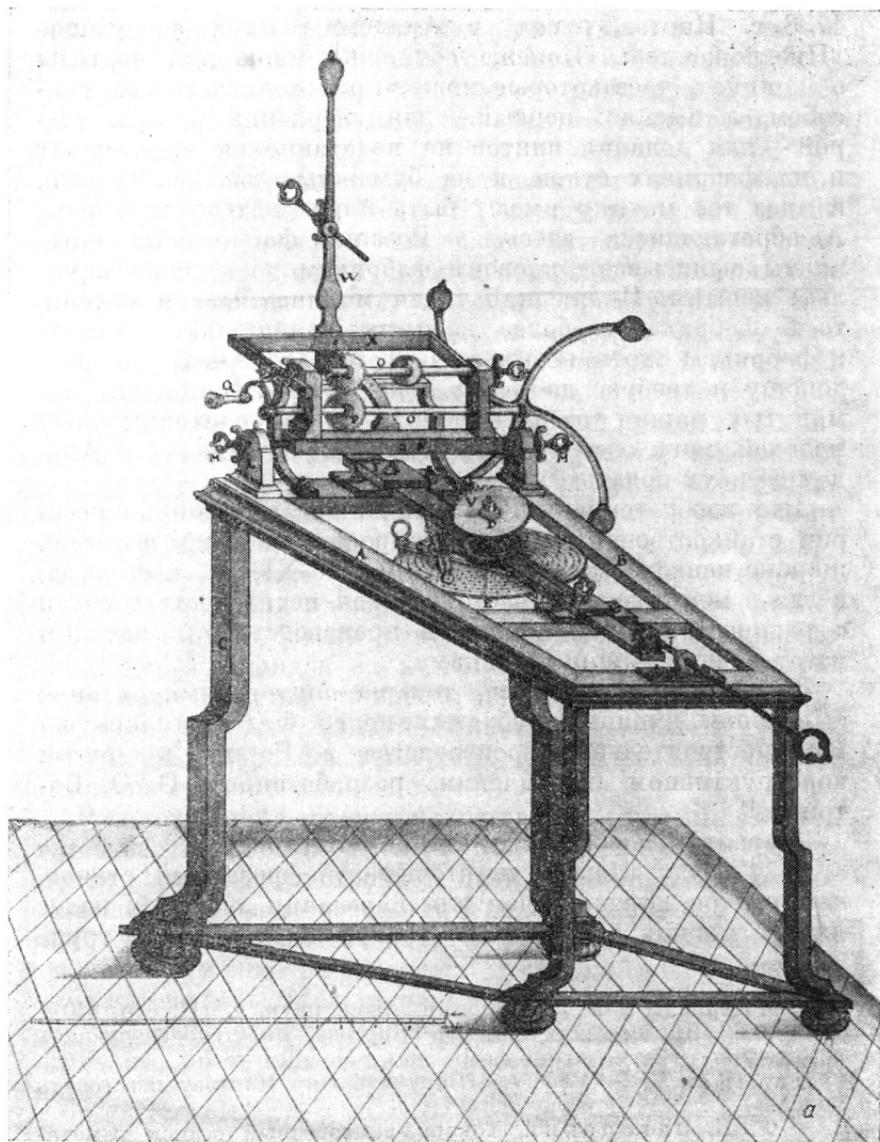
Зубофрезерный станок («Театрум махинарум»).
